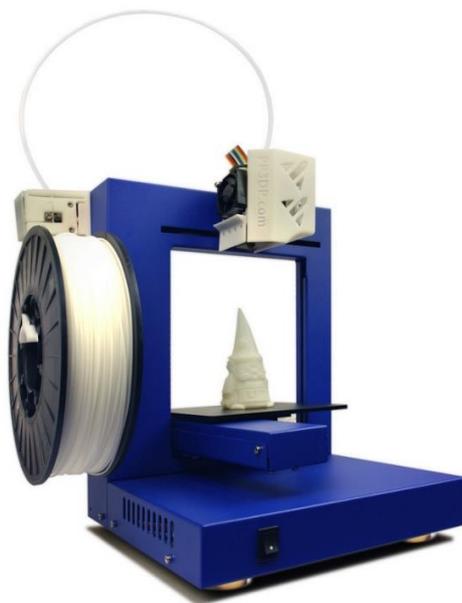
Внешний вид принтера UP! 3D Printer
